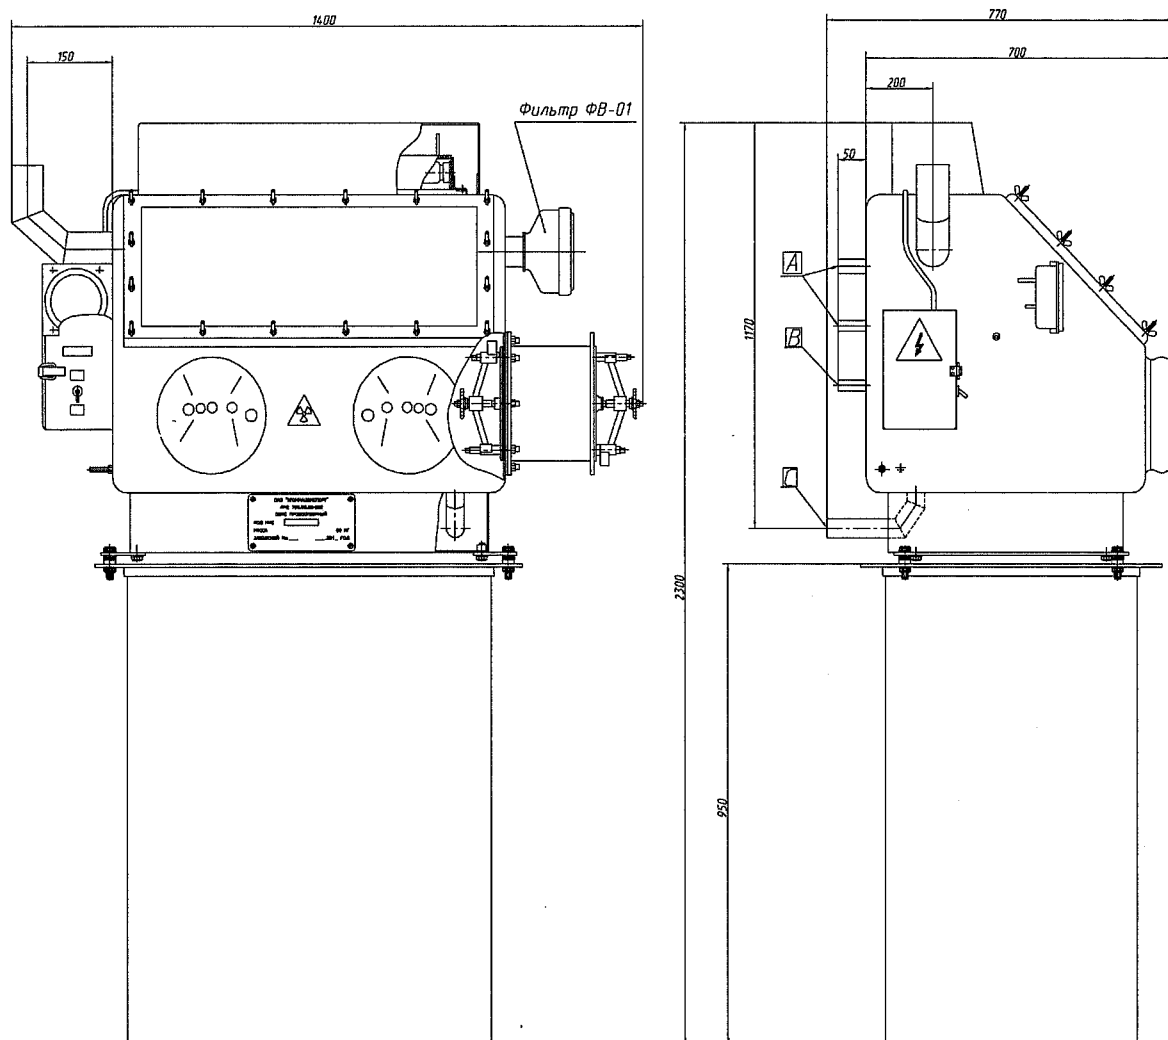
Габаритный чертеж бокса пробоотборного
